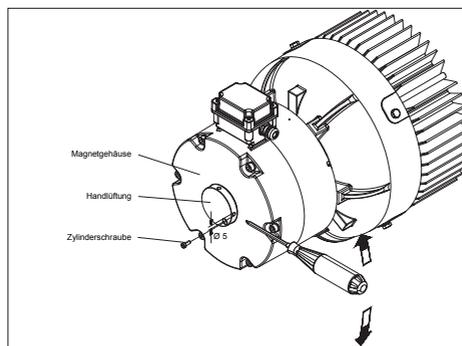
Bremse - Typen E../Z..075 und Z..100 - mit arretierbarer Handlüftung
